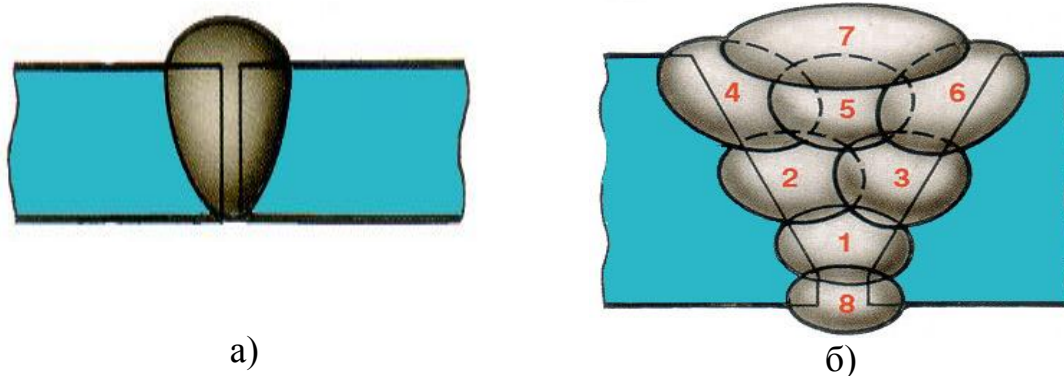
Виды сварных швов по количеству наплавленных валиков:
